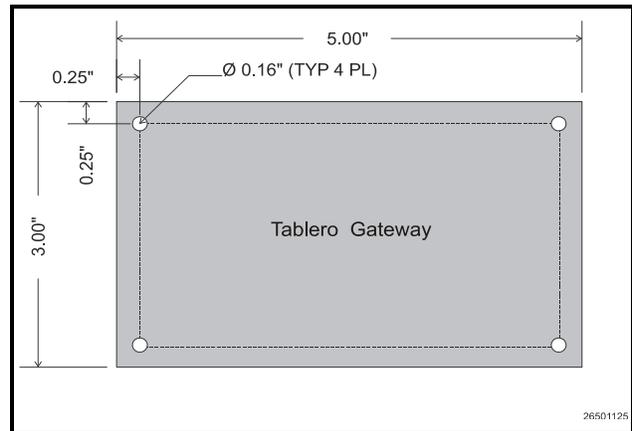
Dimensiones de Montaje del Tablero Gateway
